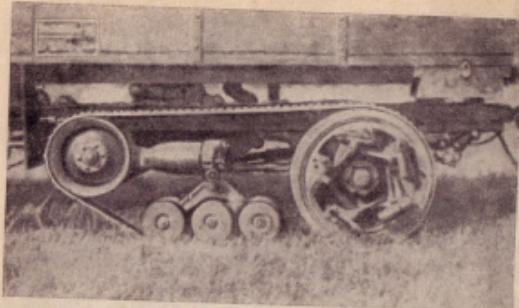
Гусеничный движитель тягача «Триангель» с добавочными шпорами на ведущем колесе (шпоры убраны внутрь).
